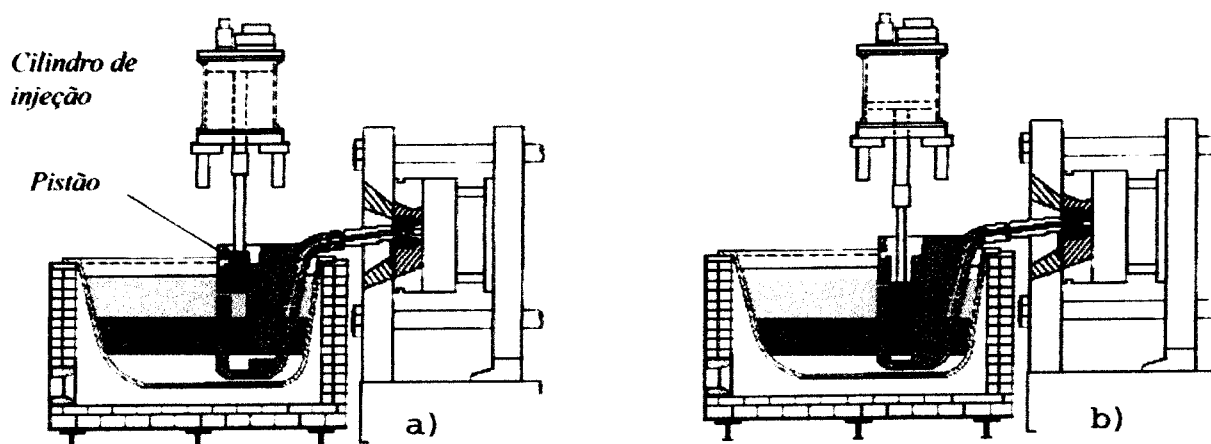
Esquema da máquina de injeção a quente; a) O pistão de injeção encontra-se em posição para iniciar a injeção do material; b) O pistão avança câmara adentro e injeta o metal para o interior do molde, segundo MALAVAZI 2005.
